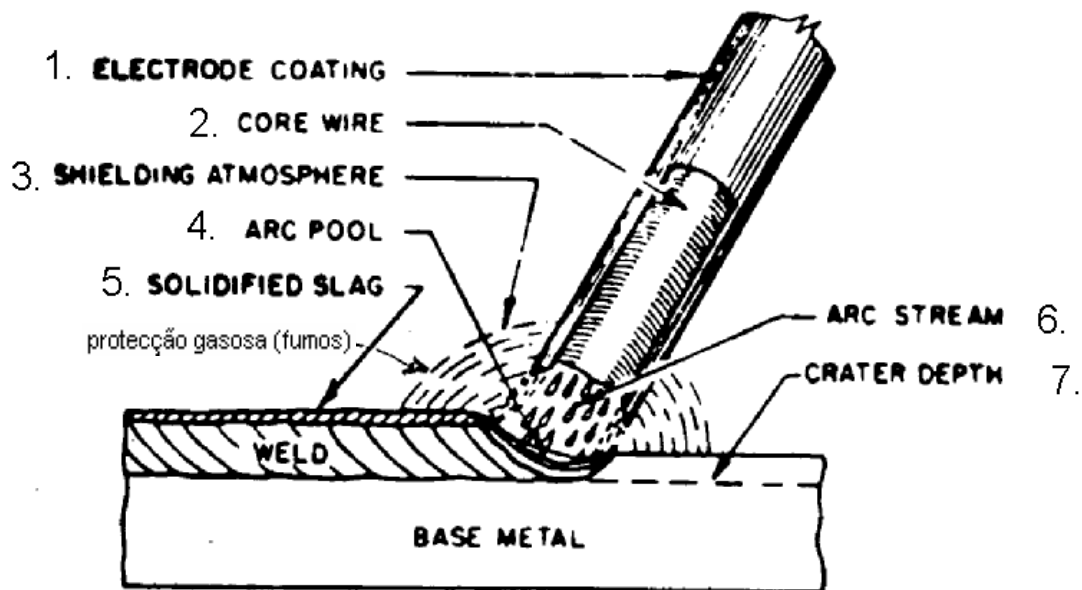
Soldadura por arco. 1-Fluxo ou revestimento; 2-alma; 3-atmosfera protectora; 4-Banho de fusão; 5-Escória; 6-Arco eléctrico e metal transferido; 7-Profundidade da cratera.
